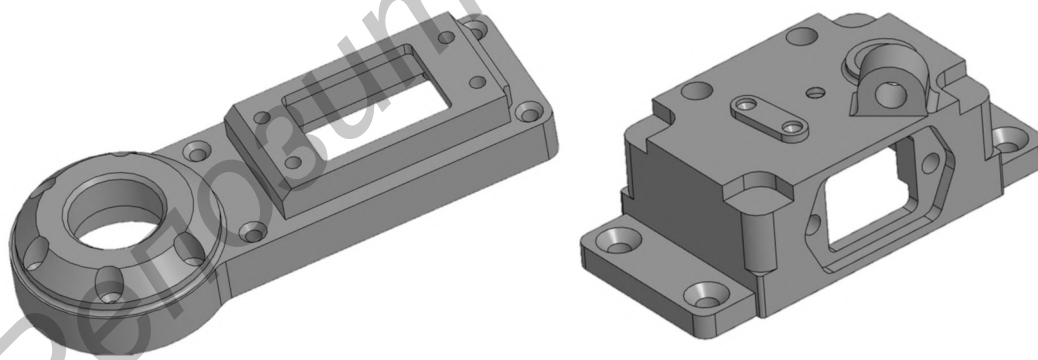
Детали «Крышка» и «Корпус разъёма»
